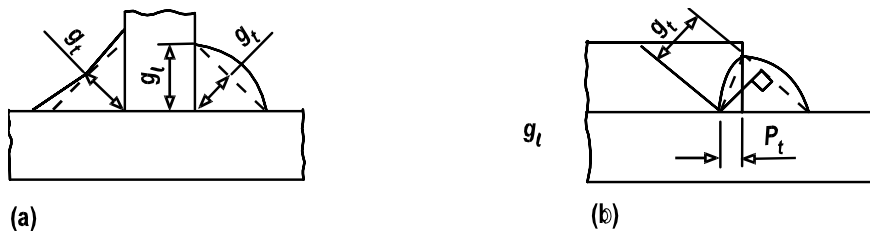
Garganta efectiva de soldaduras a tope
